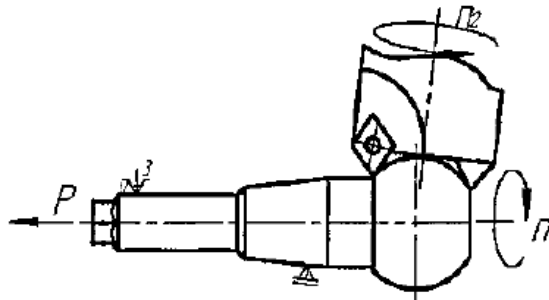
Схема фрезерування сферичної поверхні кульового пальця
